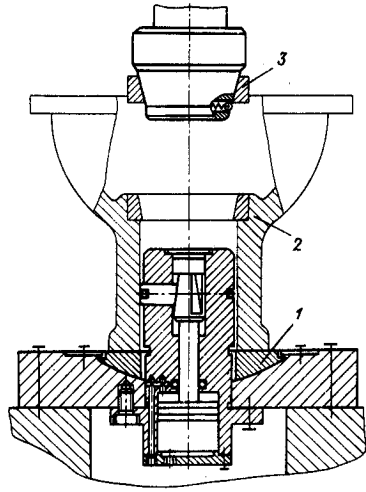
Приспособление для запрессовки наружного кольца роликоподшипника, обеспечивающее самоустановку корпуса
